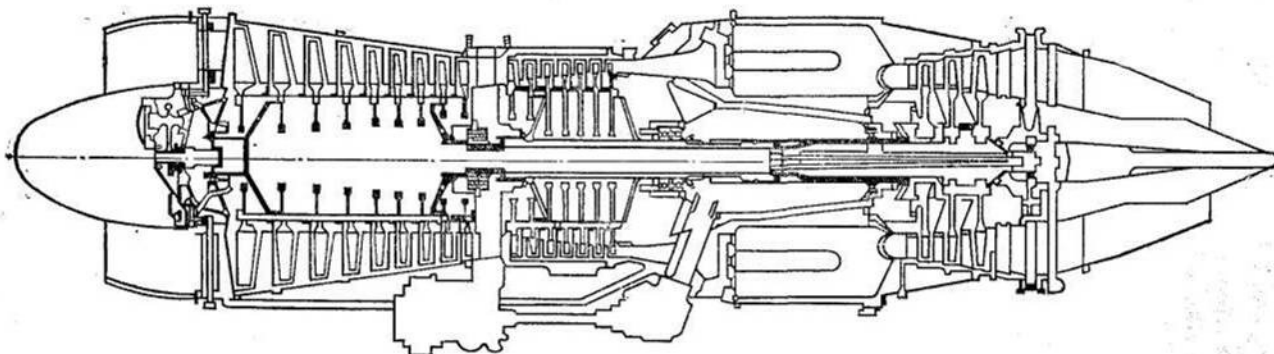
Схема типичного ТРД (двигатель J57-P-3)
